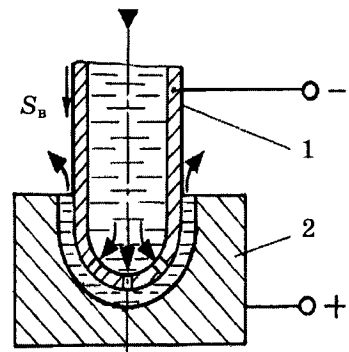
Схема електрохімічної розмірної обробки: 1 — інструмент-катод; 2 — заготовка-анод
